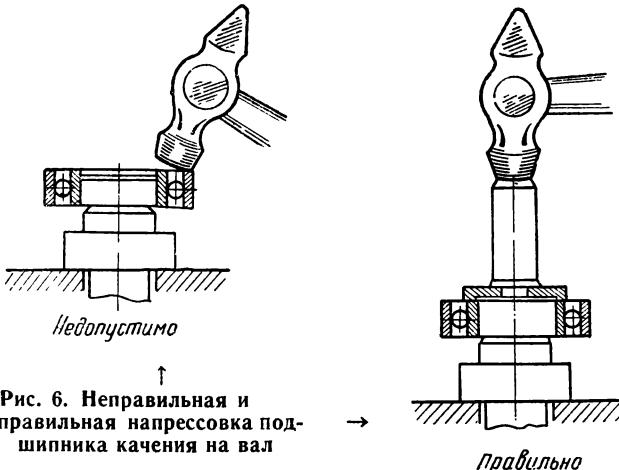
Неправильная и правильная напрессовка подшипника качения на вал
